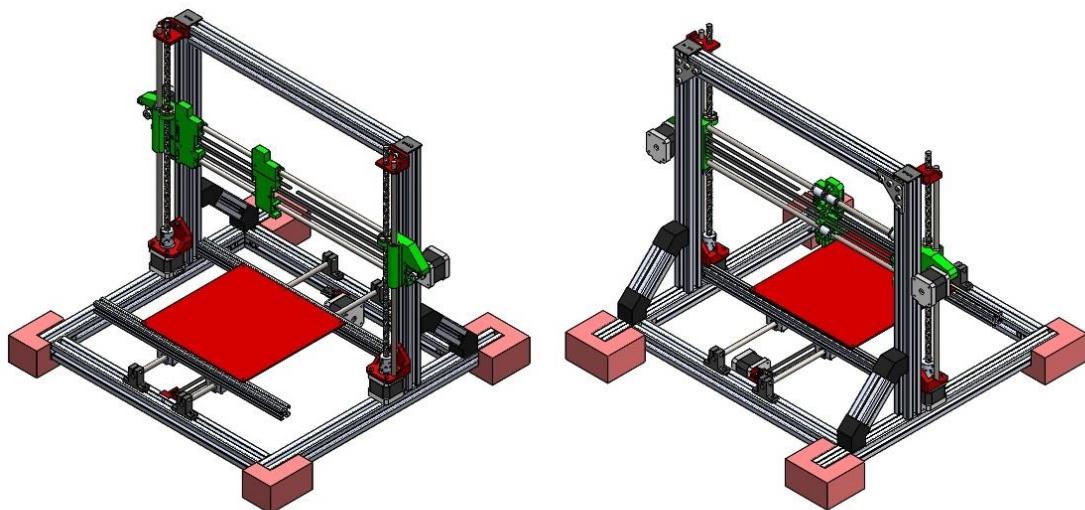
Ensamblaje estructura con los 3 ejes doble carro; Fuente: Elaboración propia con SW
